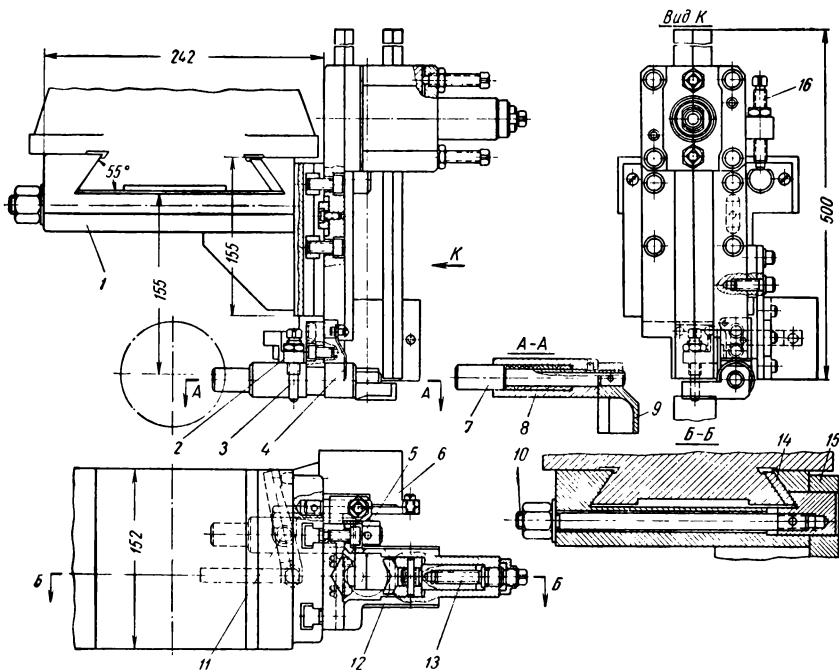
Магазинное устройство для загрузки цилиндрических заготовок диаметром от 12 до 36 мм
